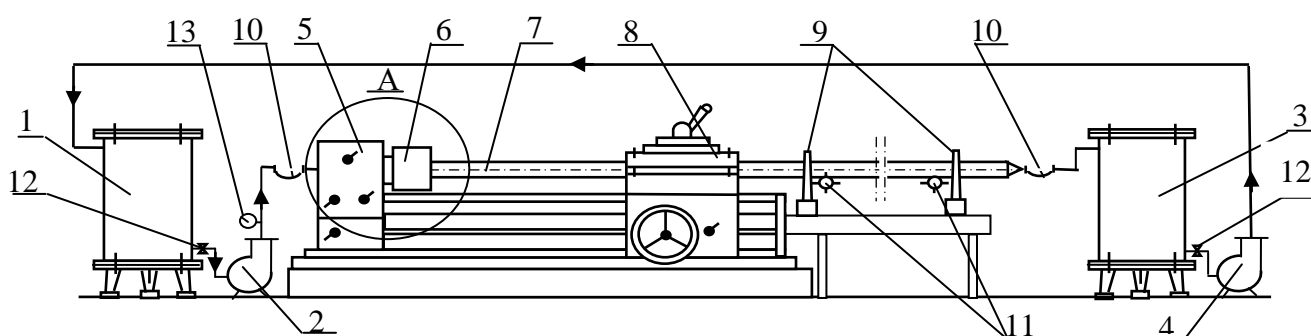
Схема полупромышленной установки для нанесения цинконола на внутреннюю поверхность труб: 1,3-питательные бочки; 2,4-насосы для перекачки краски; 5-установка для закрепления и вращения труб; 6-патрон установки; 7- труба; 8-вращающийся держатель труб; 9-выбрасыватели покрашенных труб; 10-шланги с вертлюгом; 11-транспортные ролики; 12-вентили; 13-манометр.
